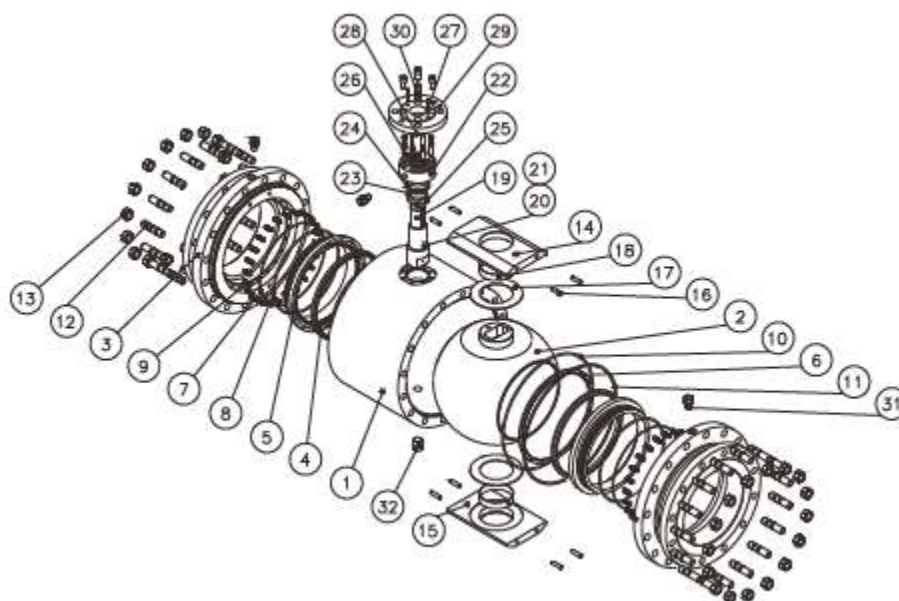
Imagine explodată de ansamblu pentru robinet cu montaj supratran
